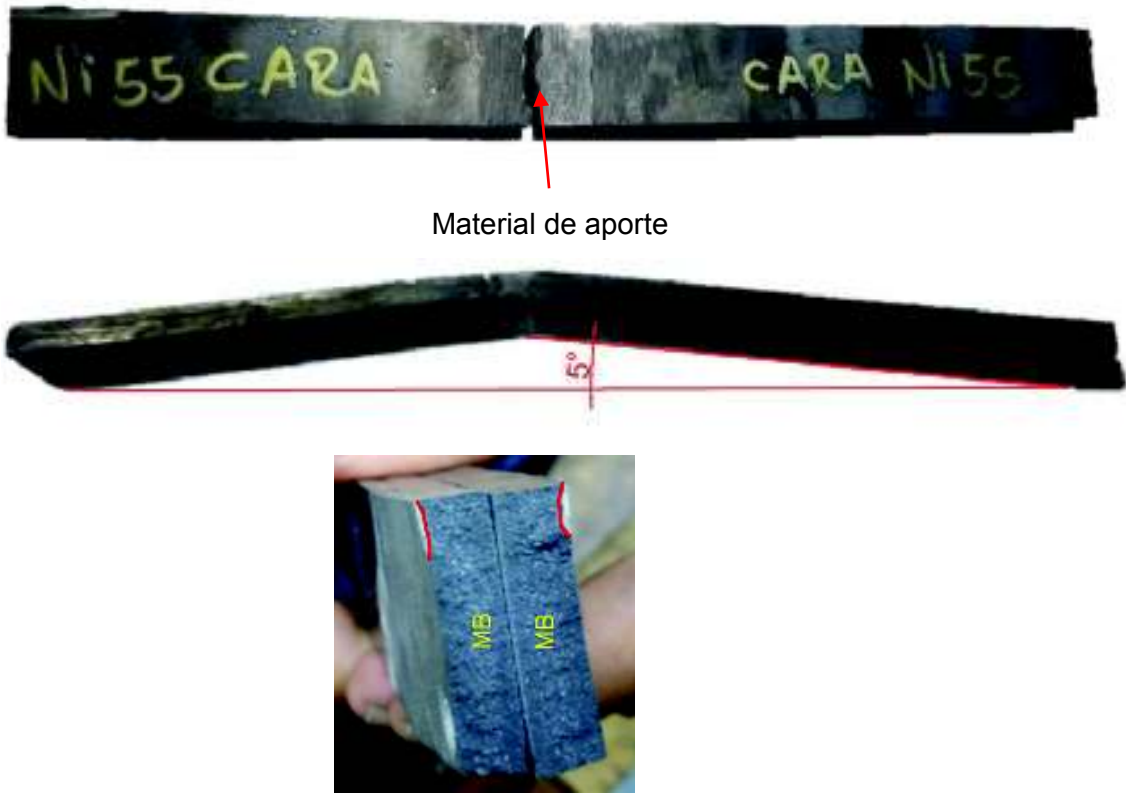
Doblado de cara de la probeta soldada con M.A. AWS E NiFe - Cl.
